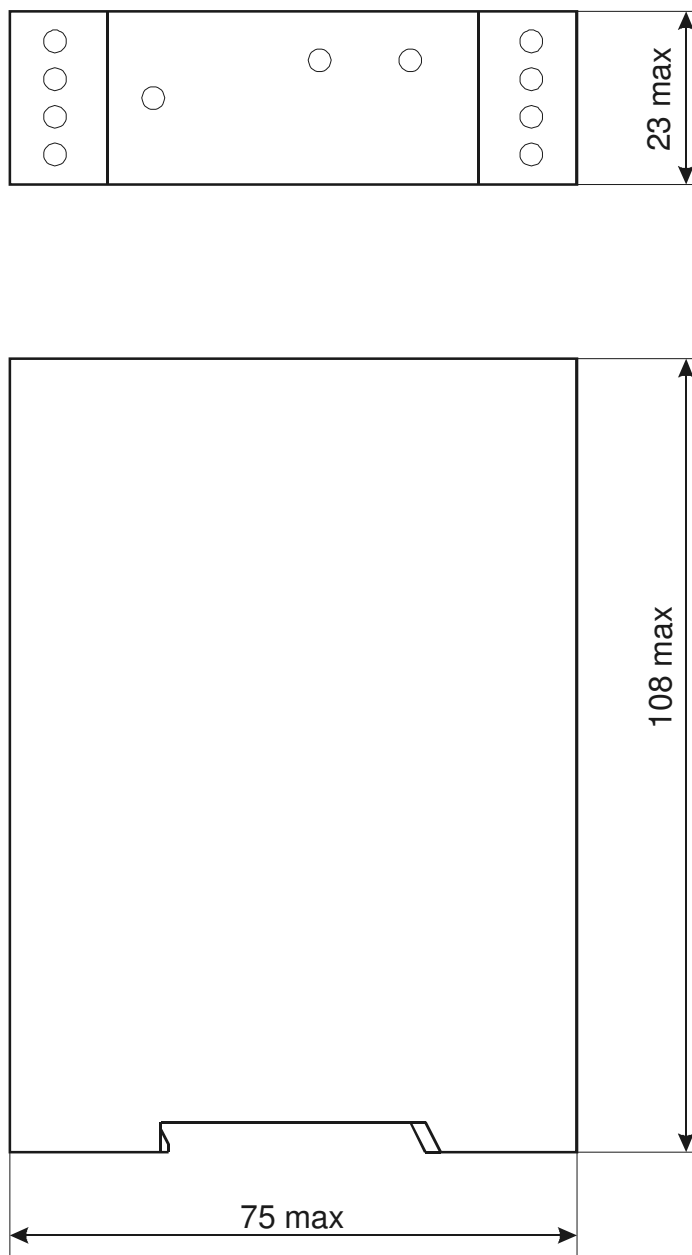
Габаритный чертеж ИП-40020-3-0, ИП-40020-3-1
